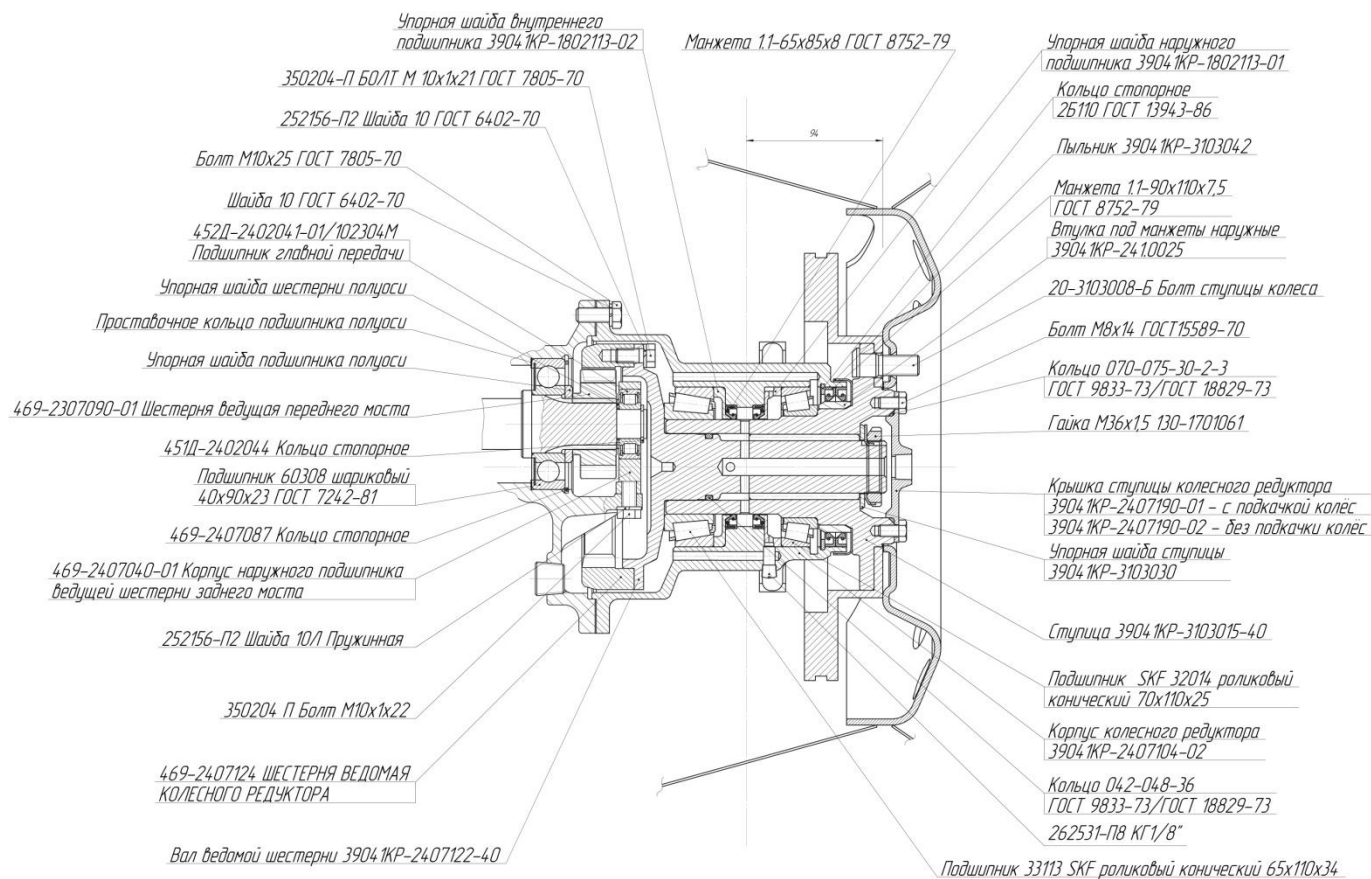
Редуктор ТРЭКОЛ-39041К
